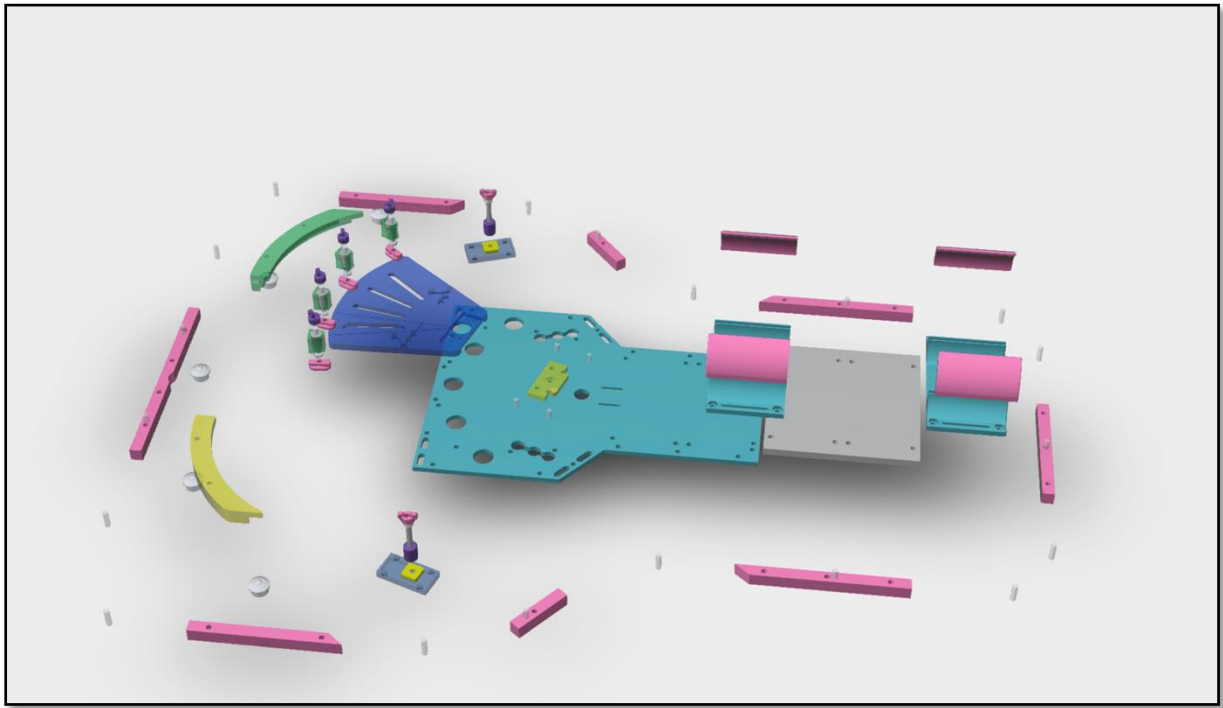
Vue 3D de l'ensemble des pièces constituant le dispositif GWMD.
